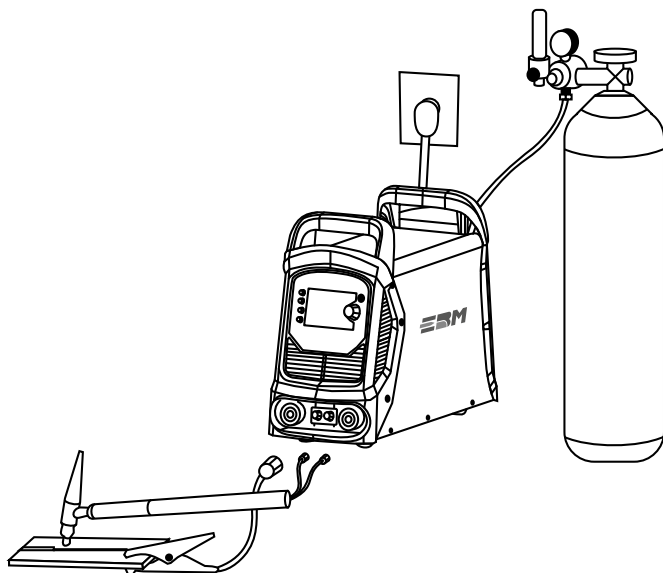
Схема подключения кабелей в режиме TIG сварки
